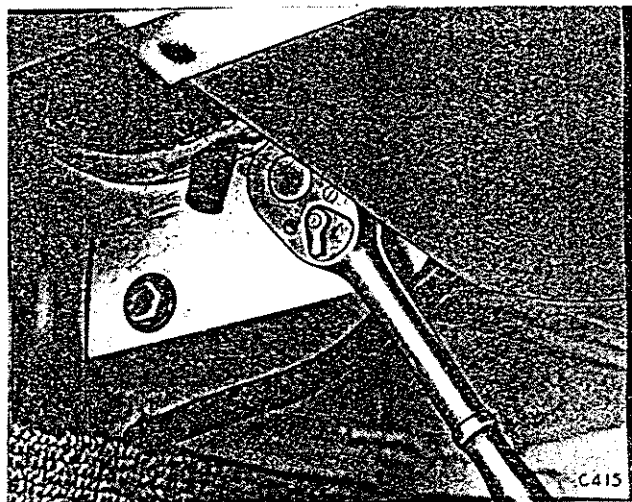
Anziehen der Halteschrauben am Motor-Tragbügel
